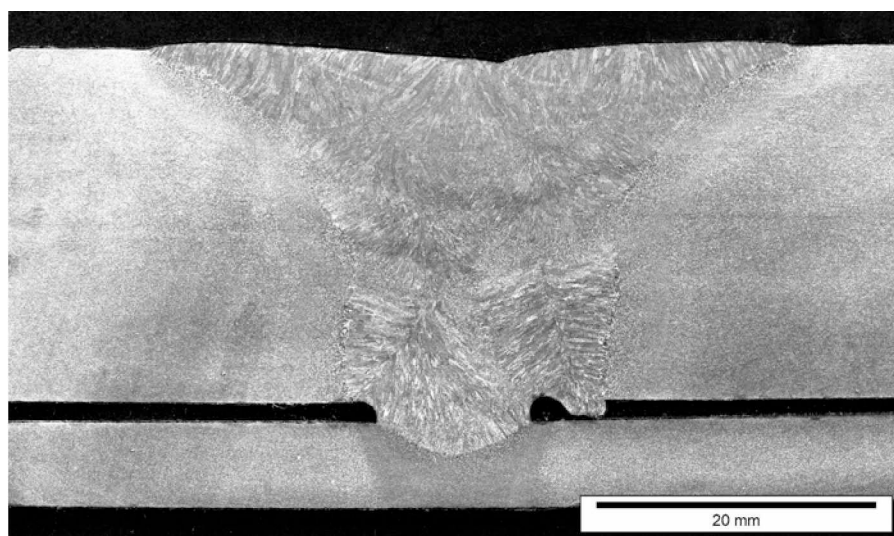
Macrografia da seção transversal da placa de teste de 25,4 mm soldada por SAW com pré-aquecimento
